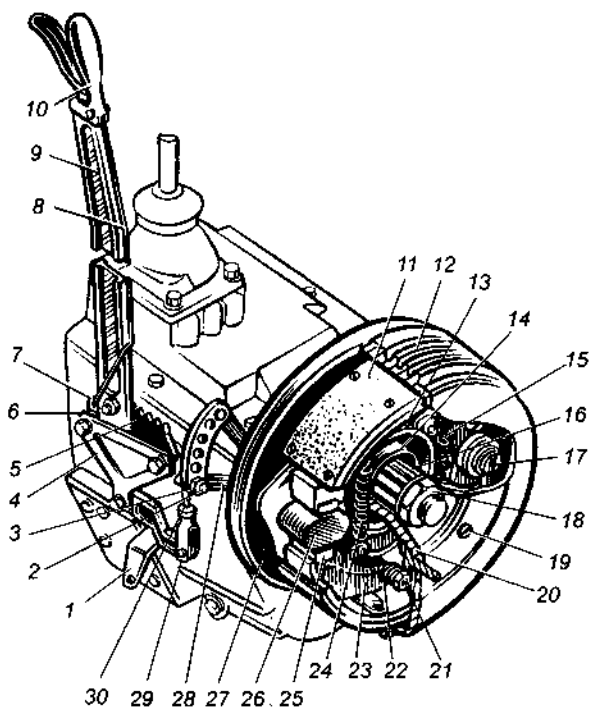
Трансмиссионный стояночный тормозной механизм: 1 — ушко тяги тормозного крана; 2 — палец тяги; 3 — гайка; 4 — пластина рычага; 5 — зубчатый сектор; 6 — распорная втулка; 7 — стопорная заселка; 8 — тяга стопорной заселки; 9 — рычаг; 10 — рукоятка тяги стопорной заселки; 11 — фрикционная накладка; 12 — барабан; 13 — кронштейн; 14 — манжета; 15, 24 — малая и большая стяжные пружины колодок соответственно; 16, 23 — колодки; 17 — ось колодок; 18 — гайка крепления фланца; 19 — винт; 20 — фланец вторичного вала коробки передач; 21 — регулировочный болт; 22 — ограничительная шайба; 25 — сухарь колодки; 26 — разжимной кулак; 27 — шит; 28 — регулировочный рычаг; 29 — вилка; 30 — тяга привода
